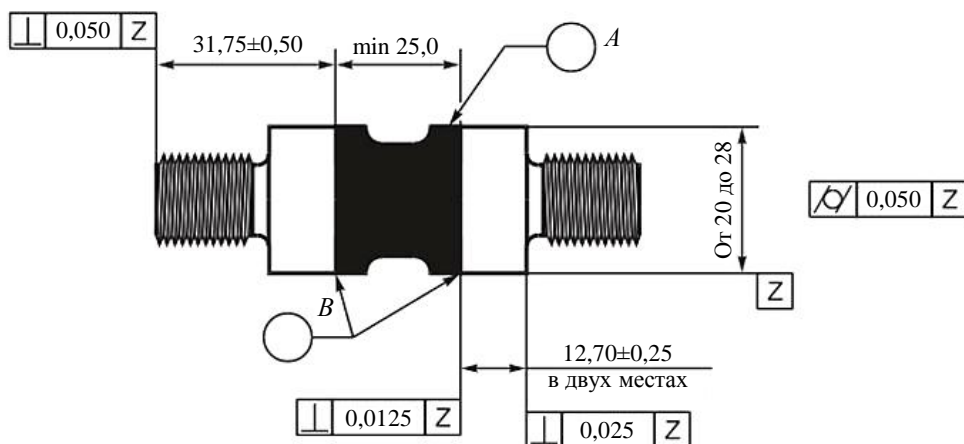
Вид образца, вклеенного в систему блоков-шпилек, подготовленного для испытаний [20]
